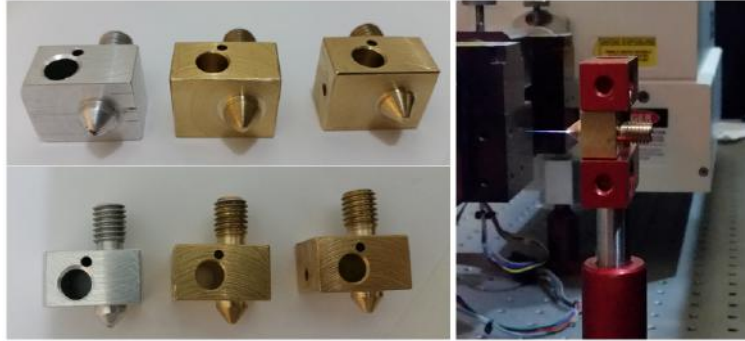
A la izquierda: Boquillas que se fabricaron. A la derecha: Micro-maquinado láser para abrirle el orificio a las boquillas.
